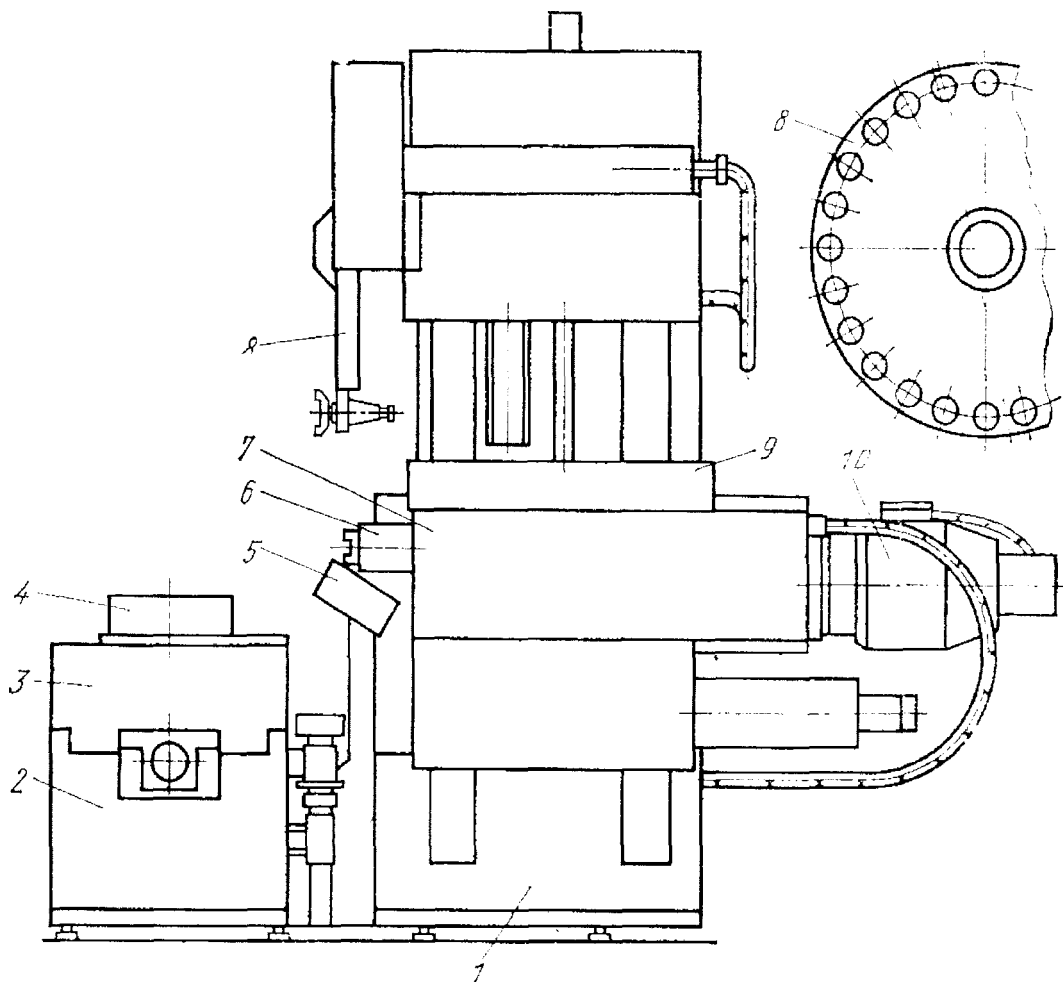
Общий вид многоцелевого станка 6305Ф4
